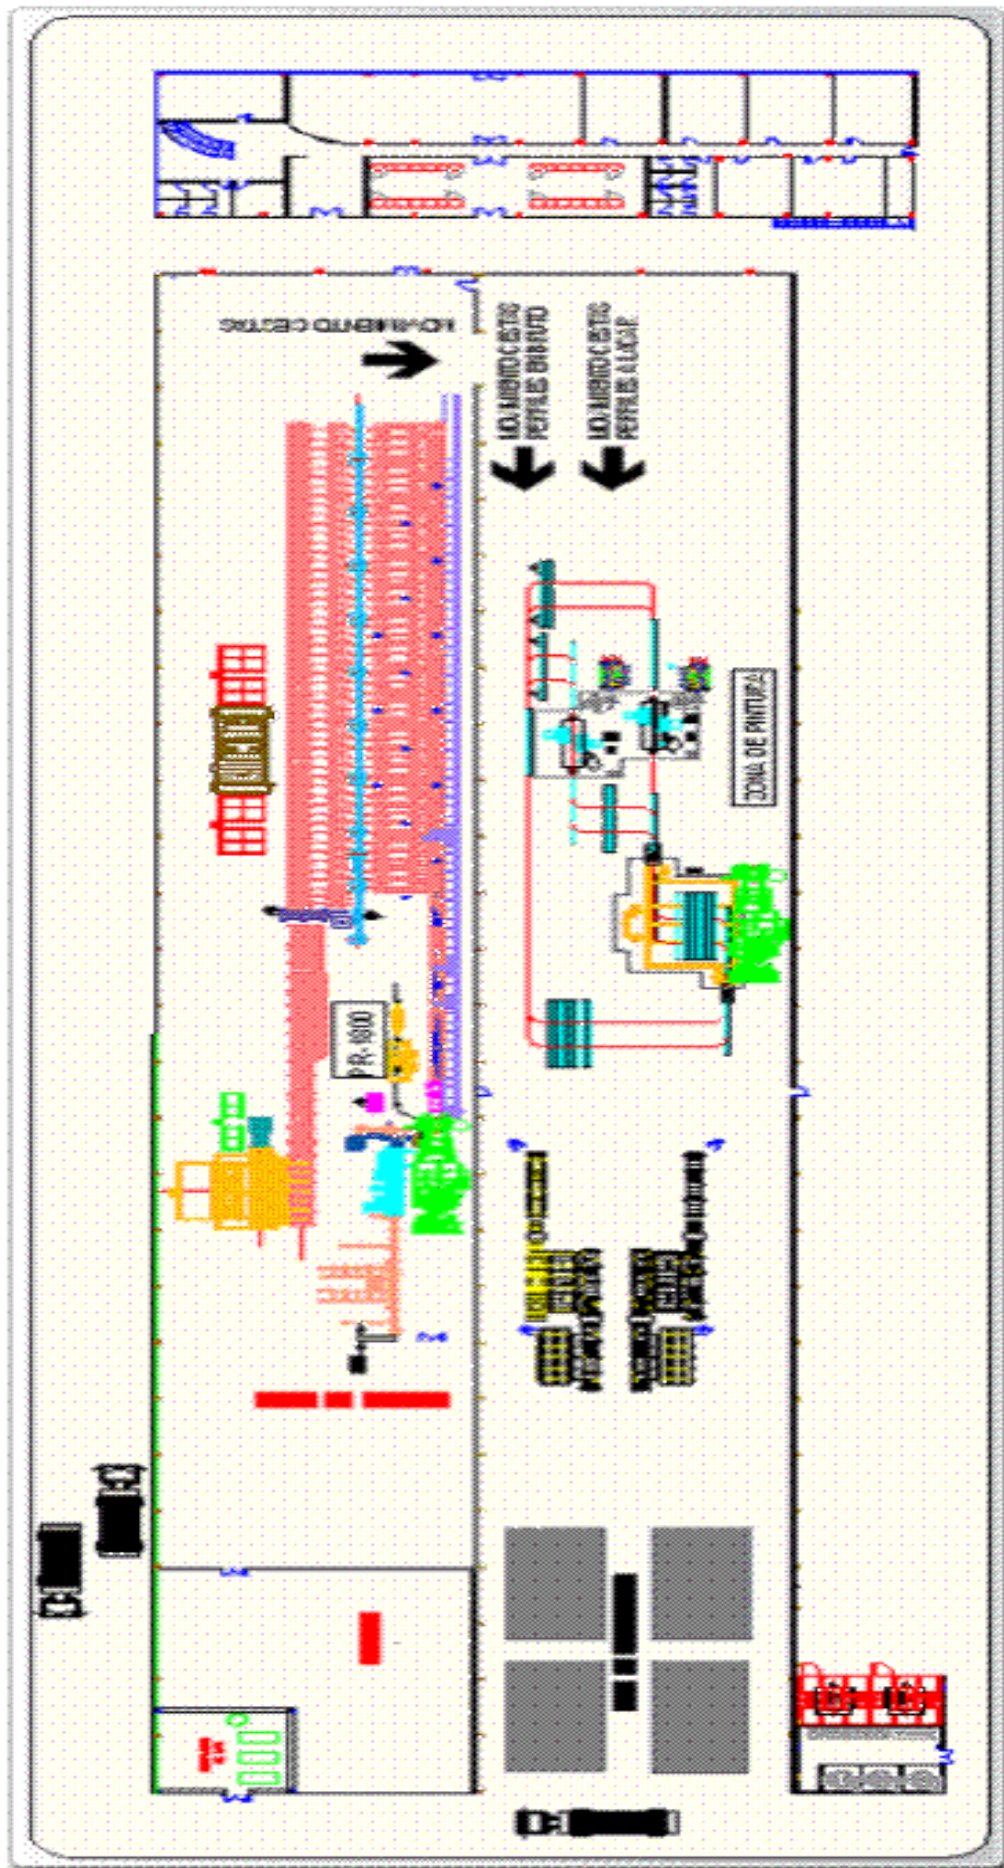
Planta de Extrusión para Perfiles de Aluminio
